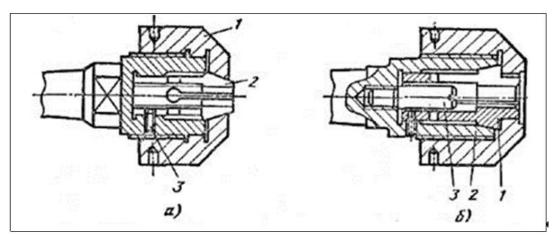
Цанговые патроны с накидной гайкой: а) цанга 2 неподвижная, б) цанга 1 подвижная
